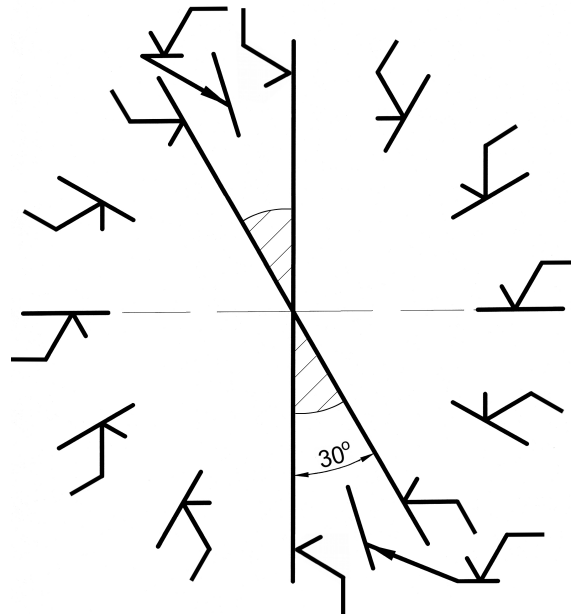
Примеры нанесения условных обозначений шероховатости
